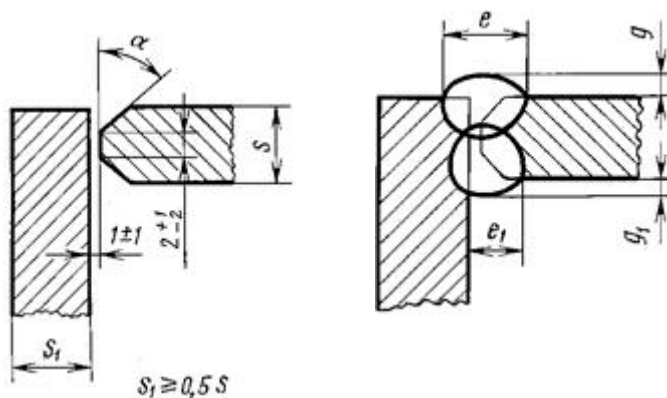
Эскиз сварного соединения У8 ГОСТ 14771-76
